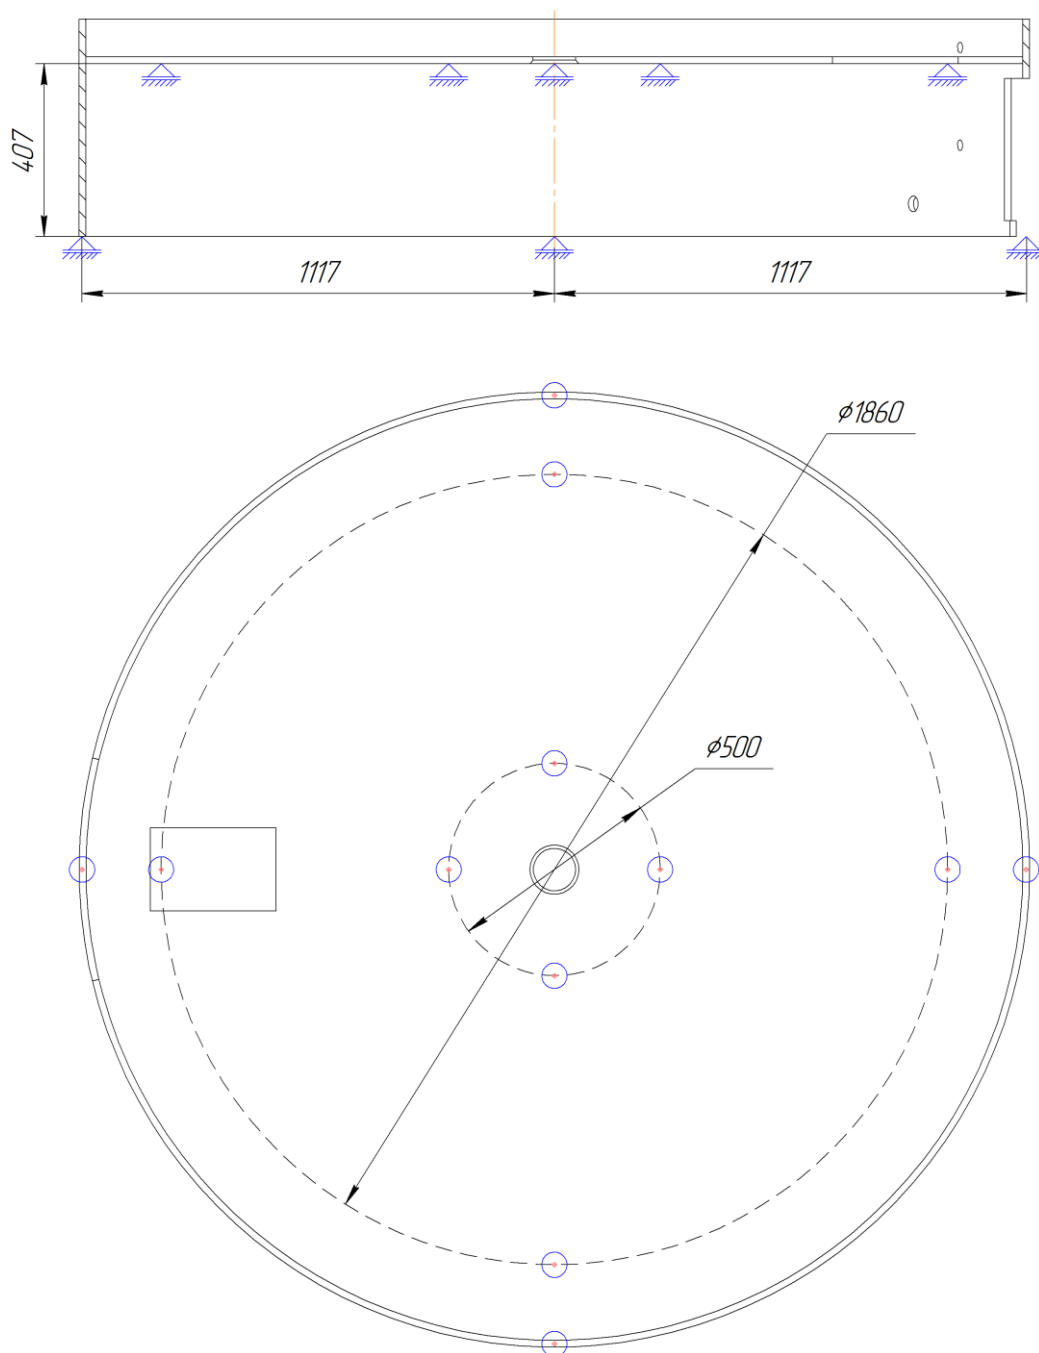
Принципиальная схема приспособления сборочно-сварочного
